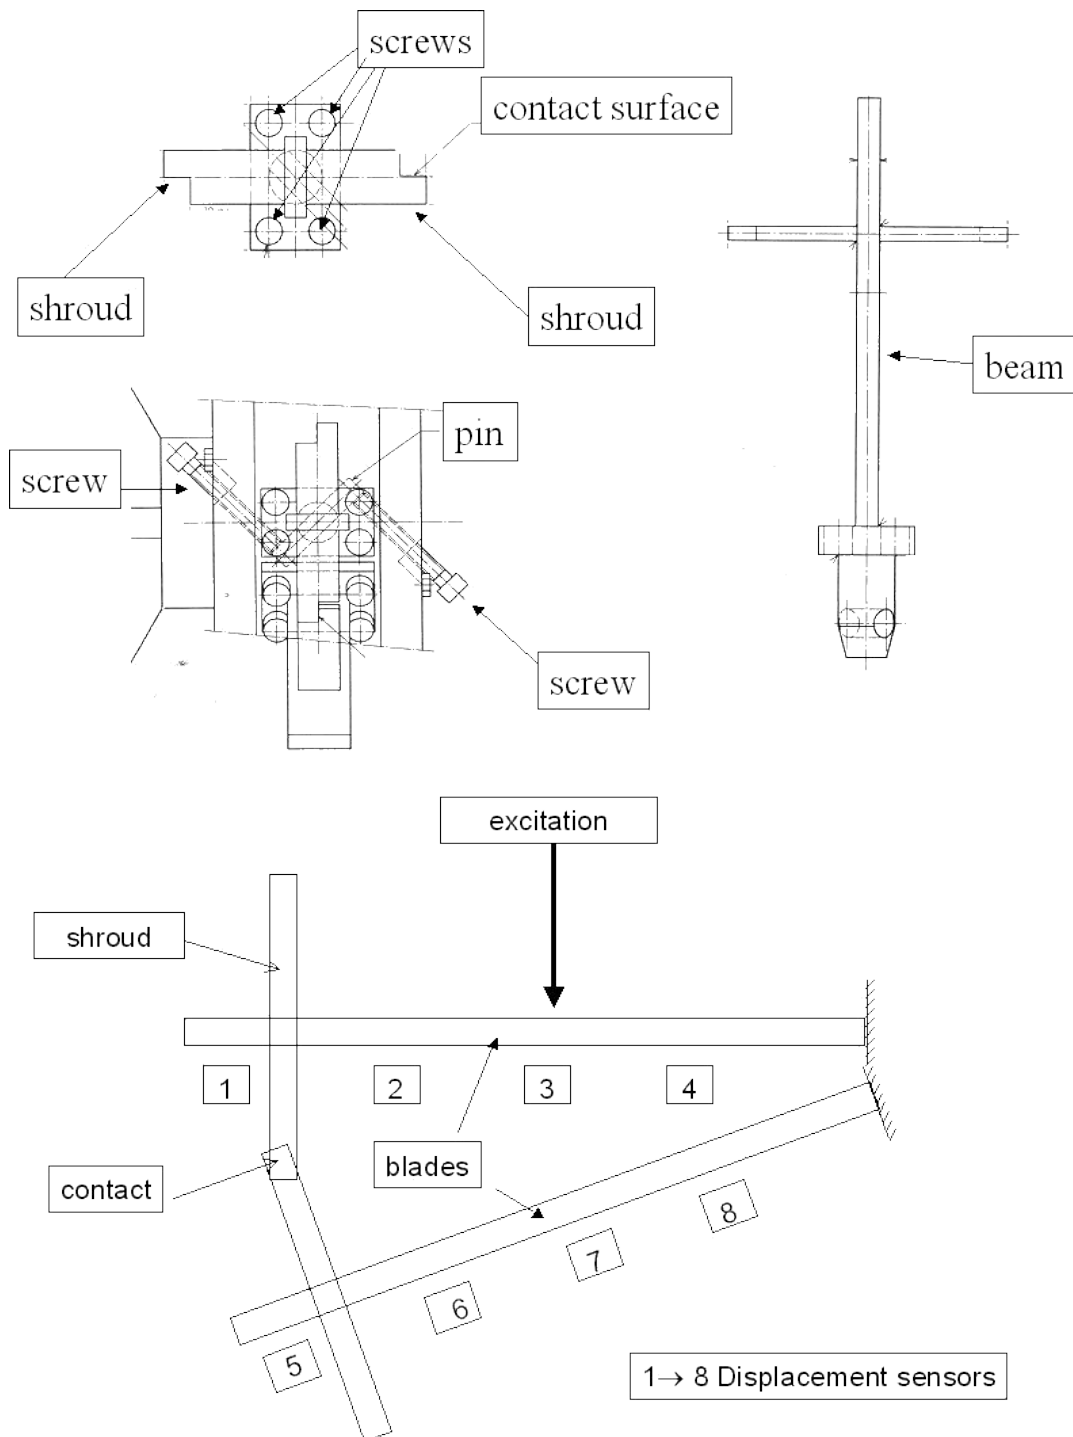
Plan des aubes et de leur instrumentation.
